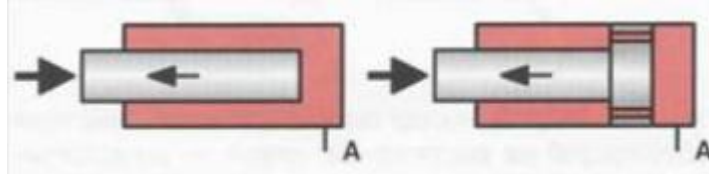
Плунжерний гідроциліндр: зліва - без внутрішнього упору, справа - з внутрішнім упором
